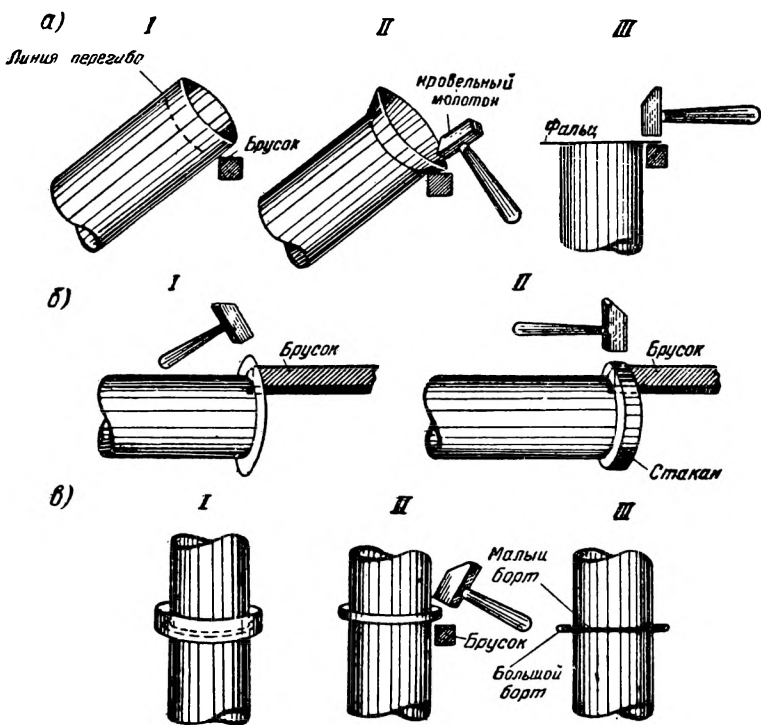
Изготовление одинарного стоячего фальца по окружности:
